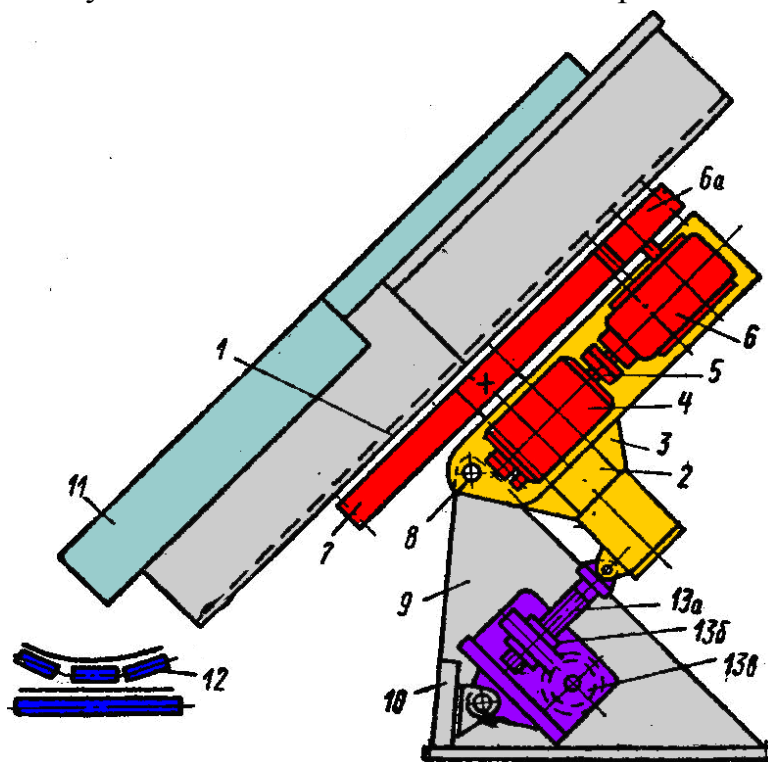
Механізми обертання і нахилу чаші чашкового огрудкувача: 1 – чаша; 2 – вращающаяся ось; 3 – опора; 4 – электродвигун постоянного тока; 5 – муфта; 6 – коническо-цилиндрический редуктор; 6а – шестерня; 7 – зубчатый венець; 8 – валики; 9 – дві стойки; 10 – поперечна балка; 11 – лоток; 12 – конвеєр; 13 а – тяга гвинт; 13 б – тяга гвинтова пара; 13 в – черв'ячна передача.
